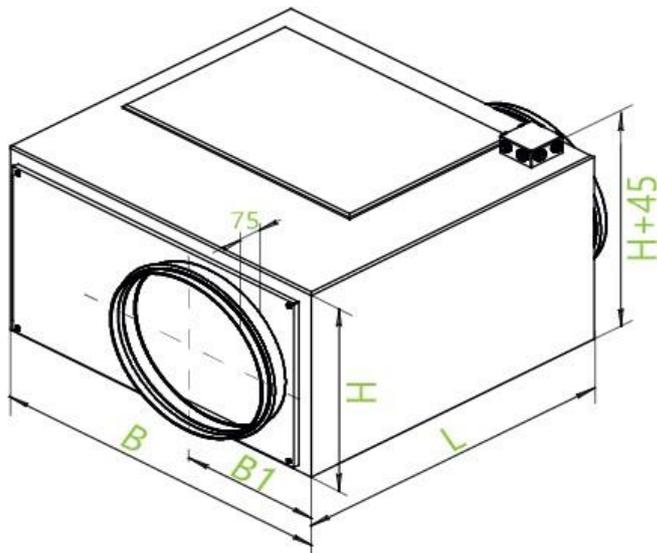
Габаритные установочные и присоединительные размеры вентиляторов
